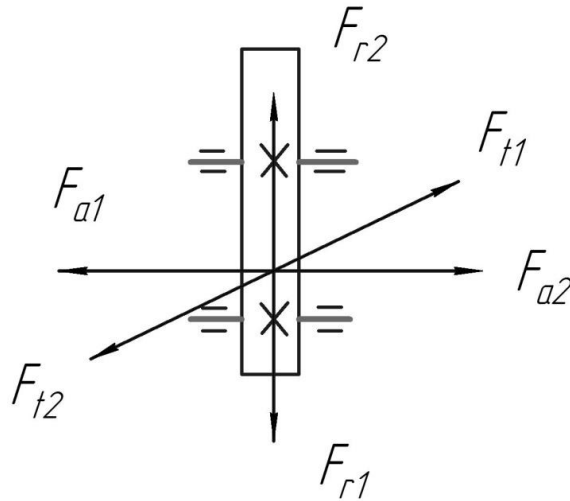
Силы в зацеплении зубчатой цилиндрической косозубой передаче
